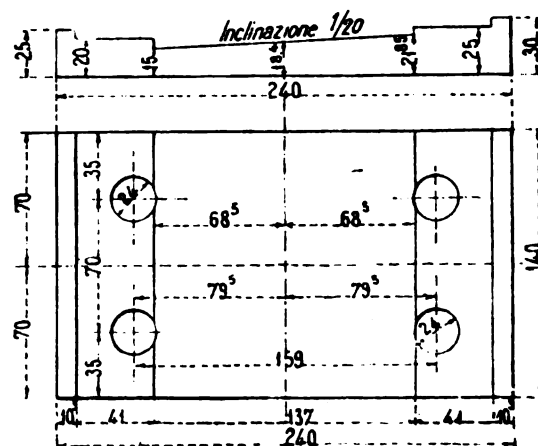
e 2. — Piastra d'appoggio delle Ferrovie dello Stato Italiano. Elevatione e pianta.
